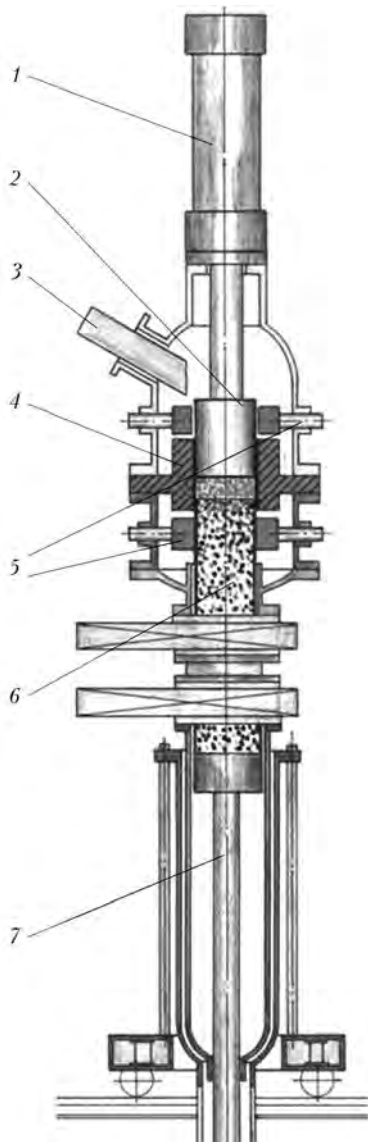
Схема установки для компактирования: 1 – гидроцилиндр; 2 – пуансон; 3 – лоток для подачи стружки; 4 – матрица; 5 – токоподводы; 6 – скомпактированная заготовка; 7 – шток
